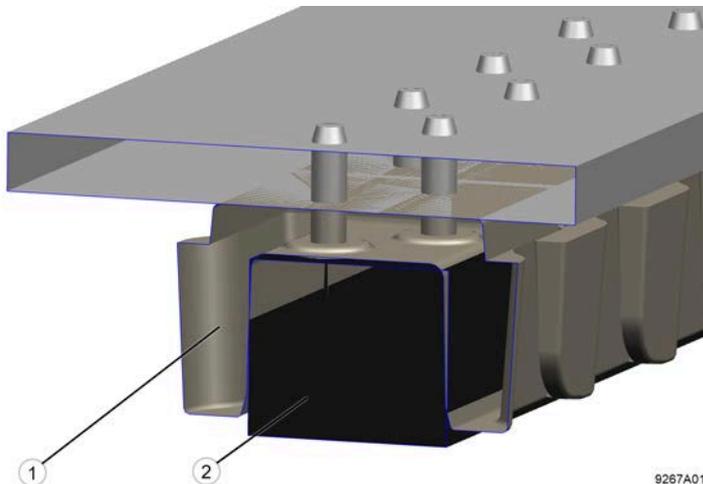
Coupe transversale de la courroie secondaire et de la chaîne à maillons
